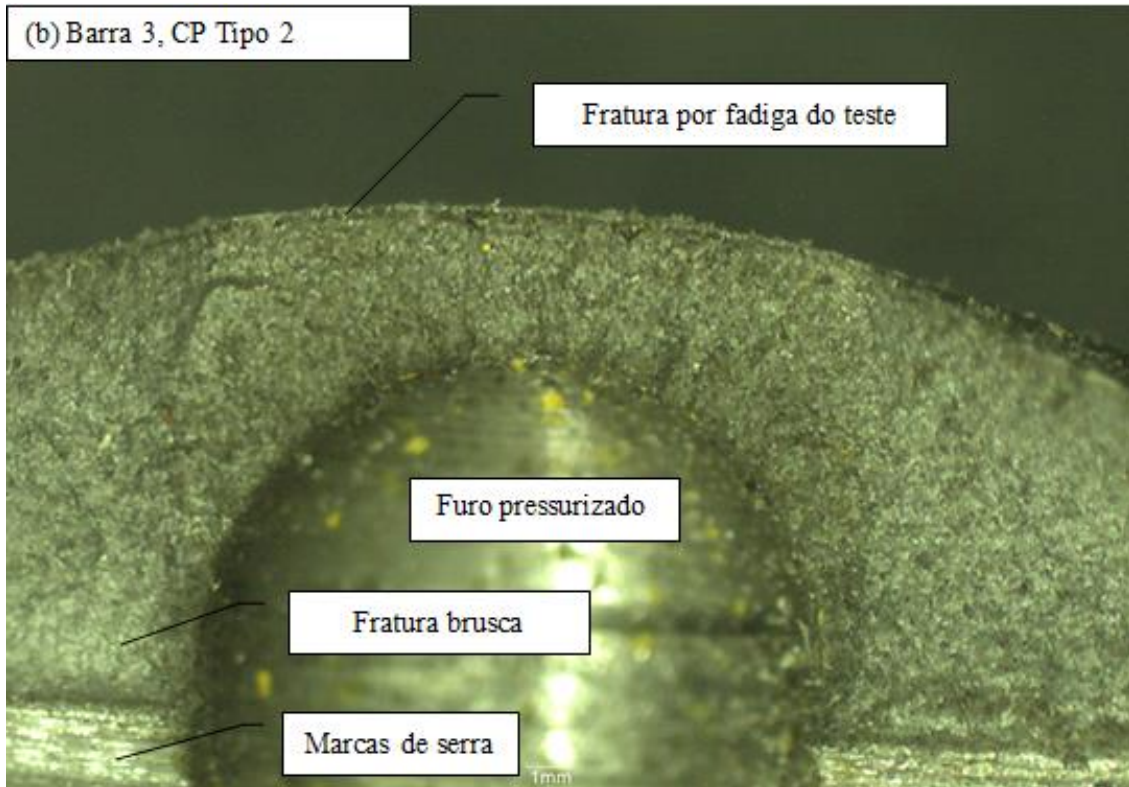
Superfície de fratura do corpo de prova tipo 2.
